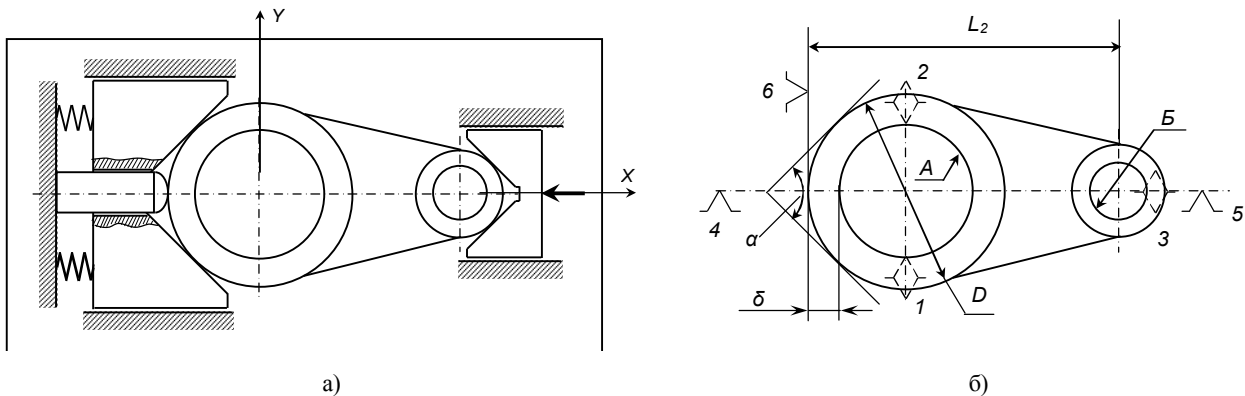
Конструктивна схема верстатного пристрою за варіантом 4 з установленою вихідною заготовкою (а) і схемою базування (б)
